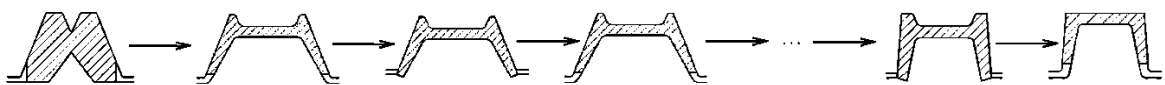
Схема швеллерной калибровки прокатных валков по корытному способу
